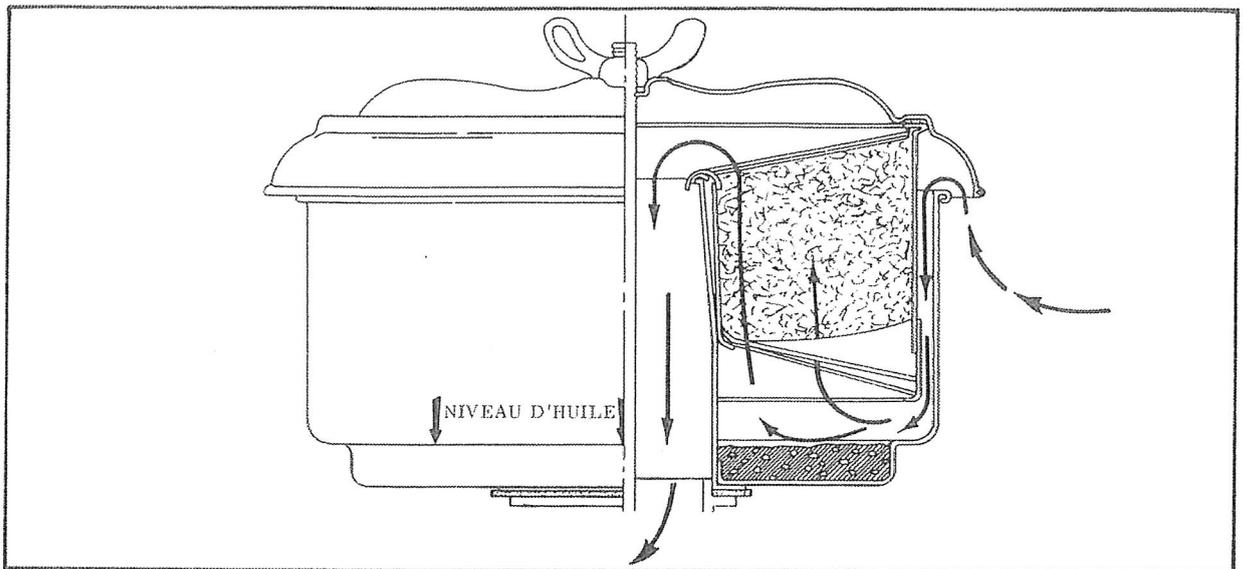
COUPE D'UN FILTRE A AIR A BAIN D'HUILE
